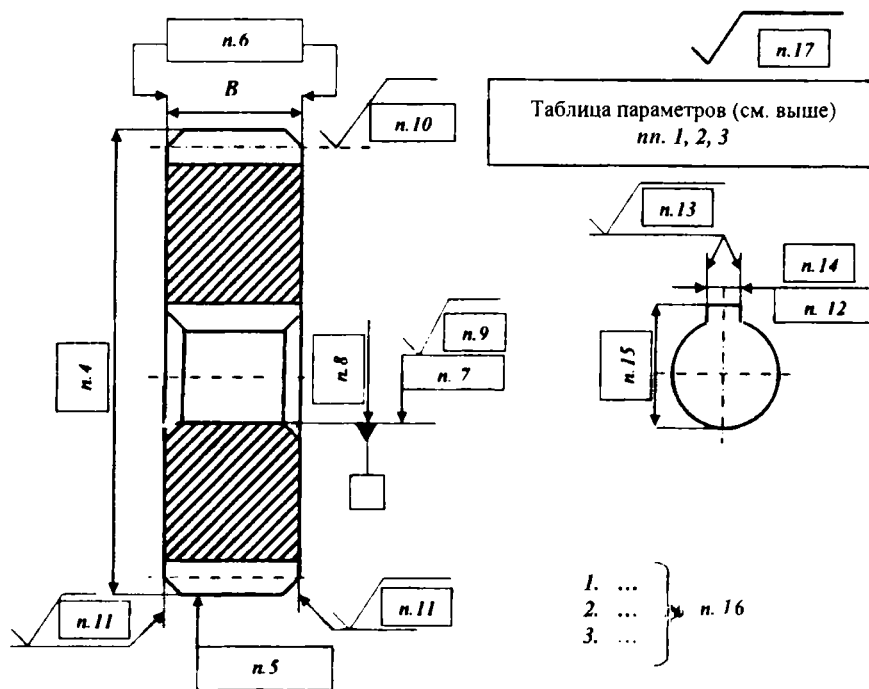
Простановка размеров и допусков на рабочем чертеже зубчатого колеса
